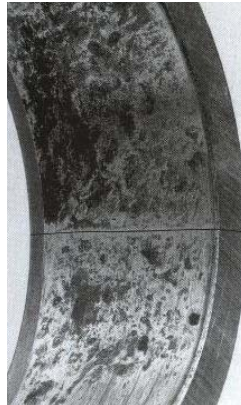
Aro interior de rodamiento de rodillos a rótula con corrosión de contacto y rotura transversal
